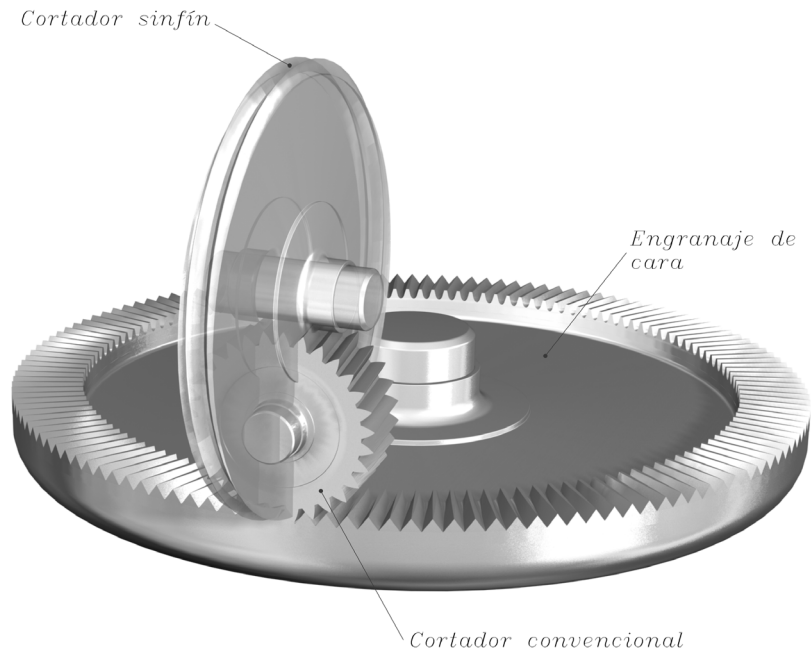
Ilustración del engranaje simultáneo del cortador sinfín, el cortador convencional y el engranaje de cara.
